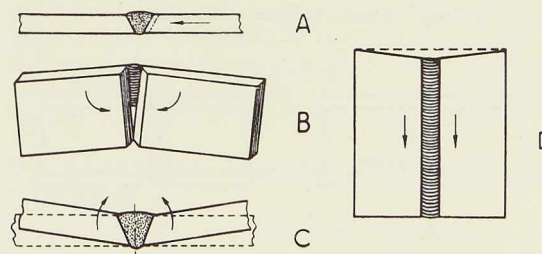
Déformations d'une soudure bout à bout.
